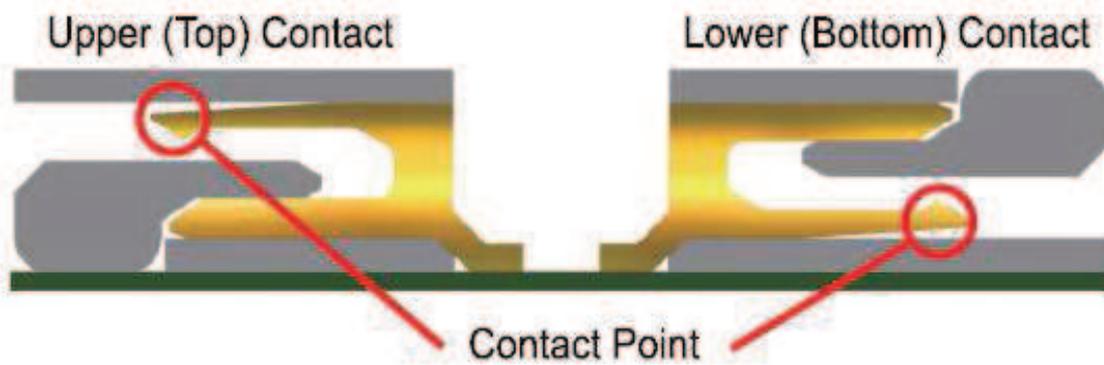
Конструкция разъемов для FFC/FPC шлейфов с верхним Top и нижним Bottom расположением контактов
